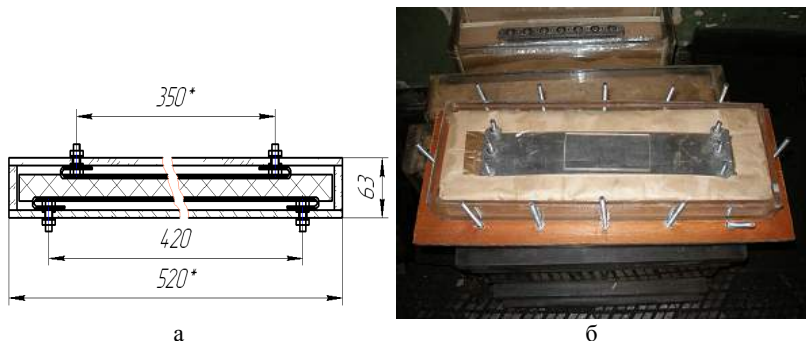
Конденсатор КИМ-134: а – габаритные размеры, б – внешний вид в состоянии изготовления на прессующем приспособлении
